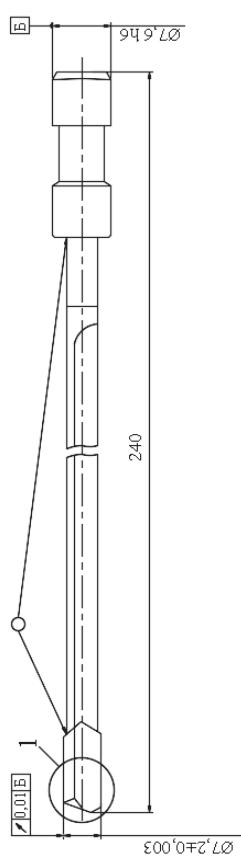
Ружейное сверло с цельнотвердосплавной головкой
